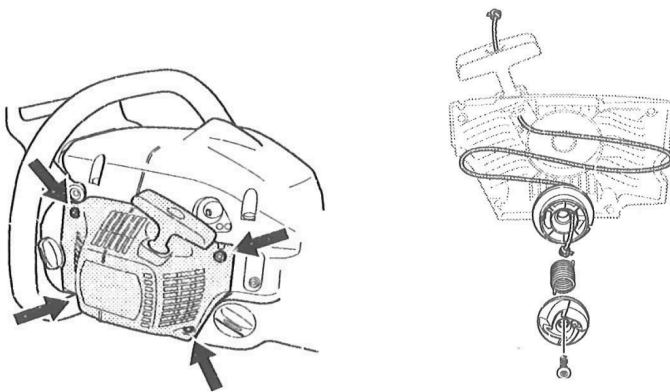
Fokussierung auf Details; Explosionszeichnung (Husqvarna 340 2005, S. 32)
